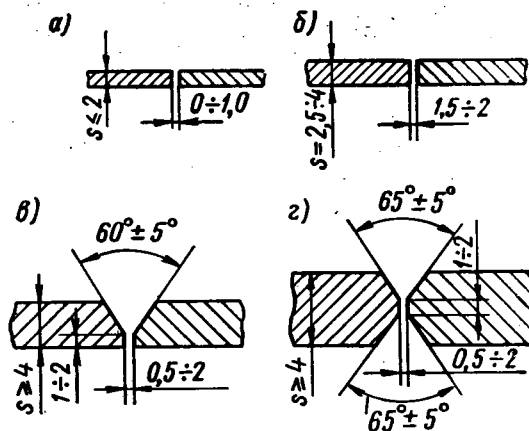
Конструктивные элементы подготовки кромок листовой стали марок 0X18H10T и X18H10T, свариваемой ручной аргоно-дуговой сваркой неплавящимся (вольфрамовым) электродом: а и б — без скоса кромок; в — V-образная разделка кромок; г — X-образная разделка кромок
